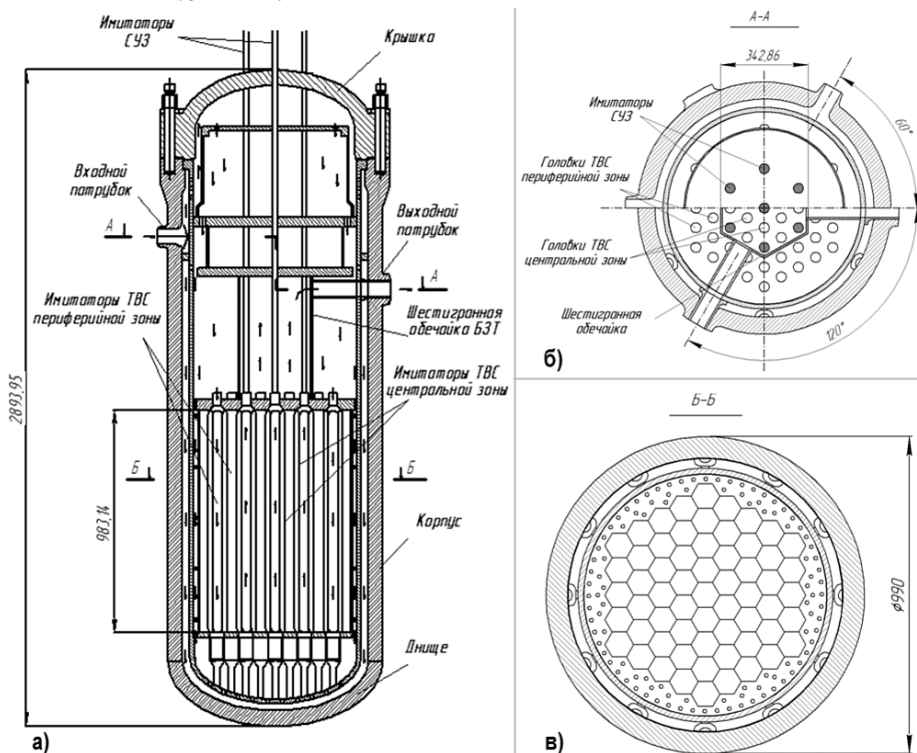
Общий вид конструкции гидравлической модели с двухходовой схемой движения
